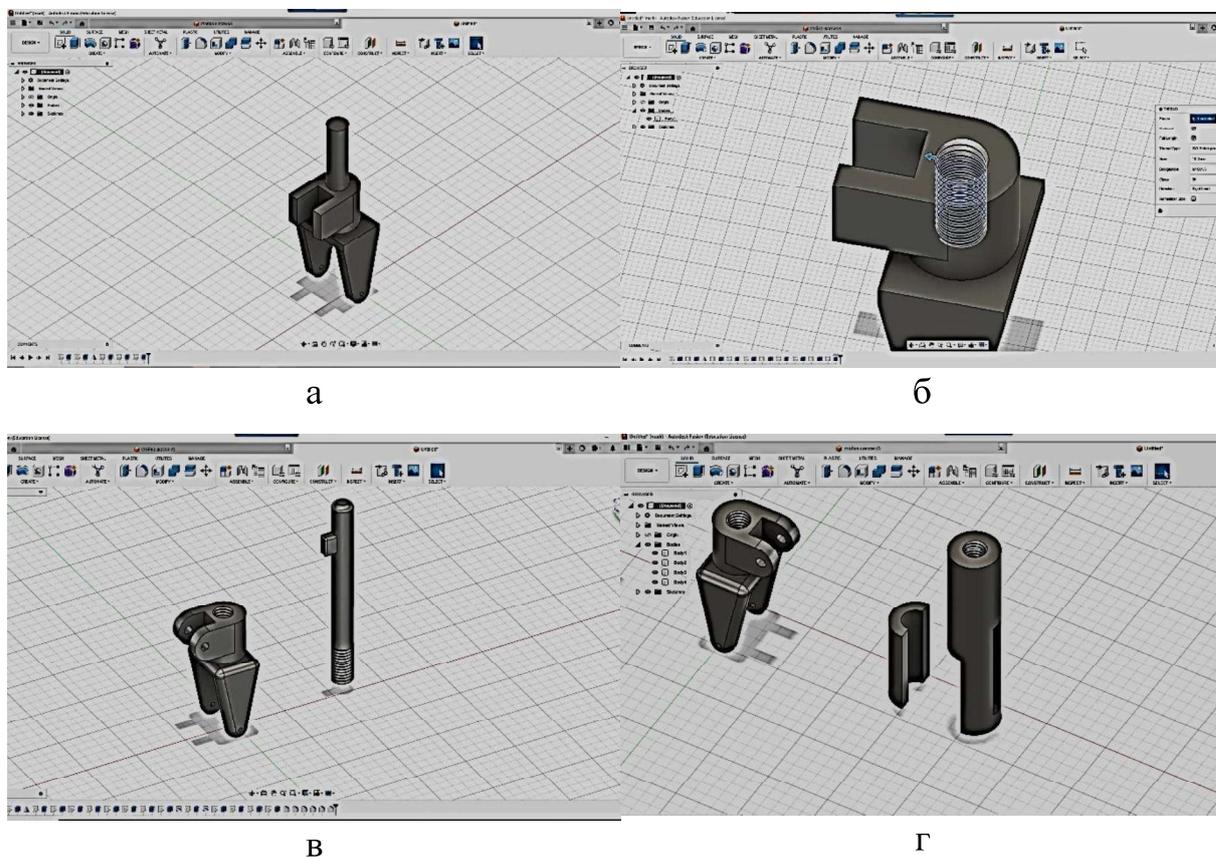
Етапи створення моделі в середовищі Fusion 360; а) основна заготовка; б) створення нарізи командою THREAD; в) закруглення кутів за допомогою команди FILLET; г) вигляд трьох деталей
